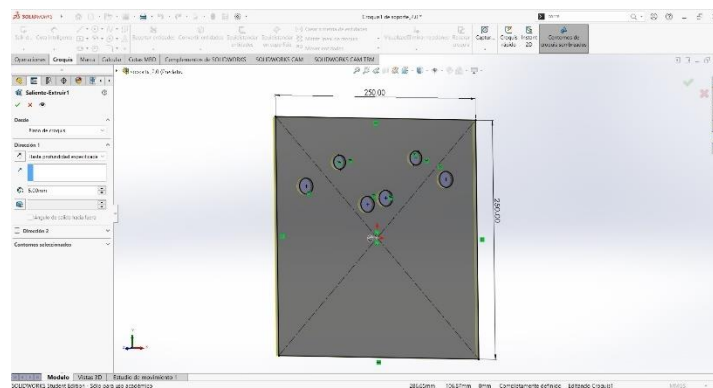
Soporte (Extrusionado). Fuente: SolidWorks
